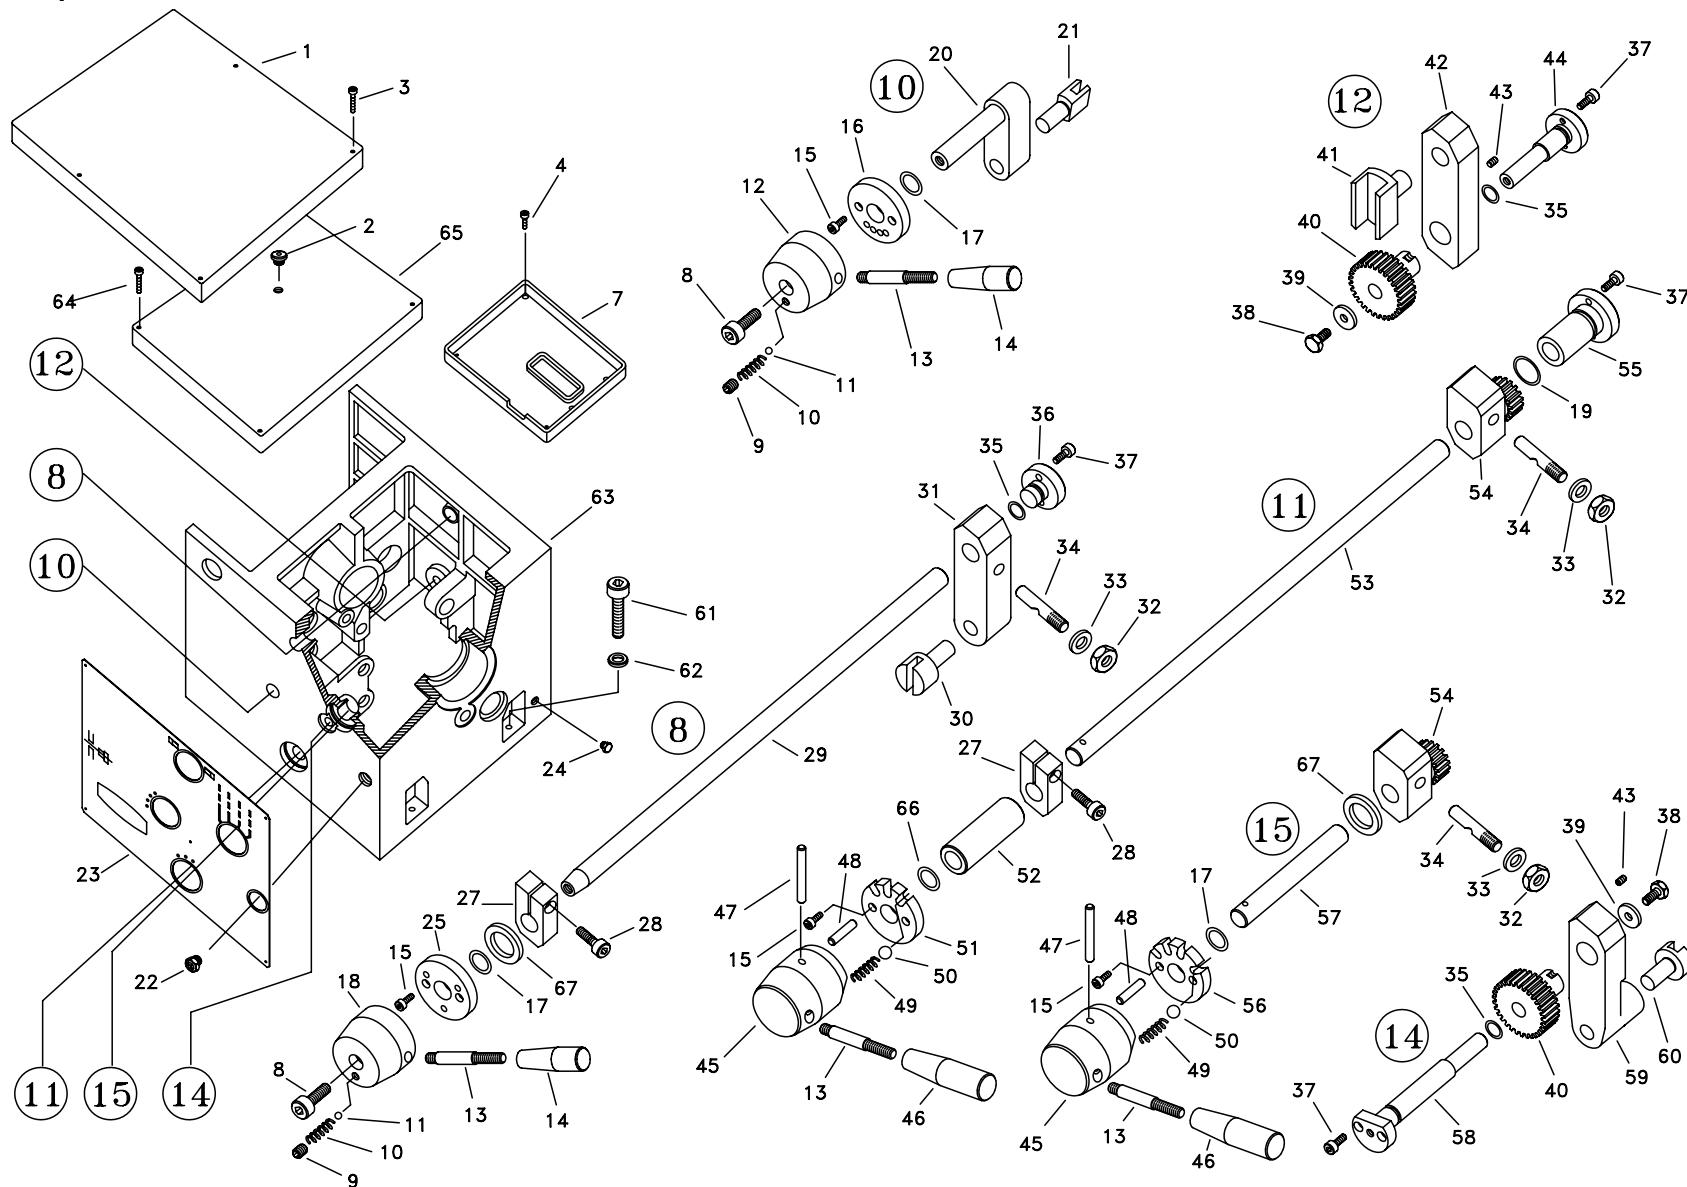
Rozpadové schéma - Vřeteník 2 ze 3
